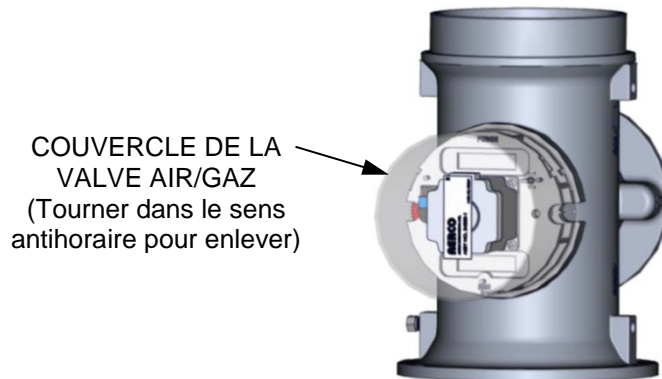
Emplacement type du couvercle de la valve air/gaz
